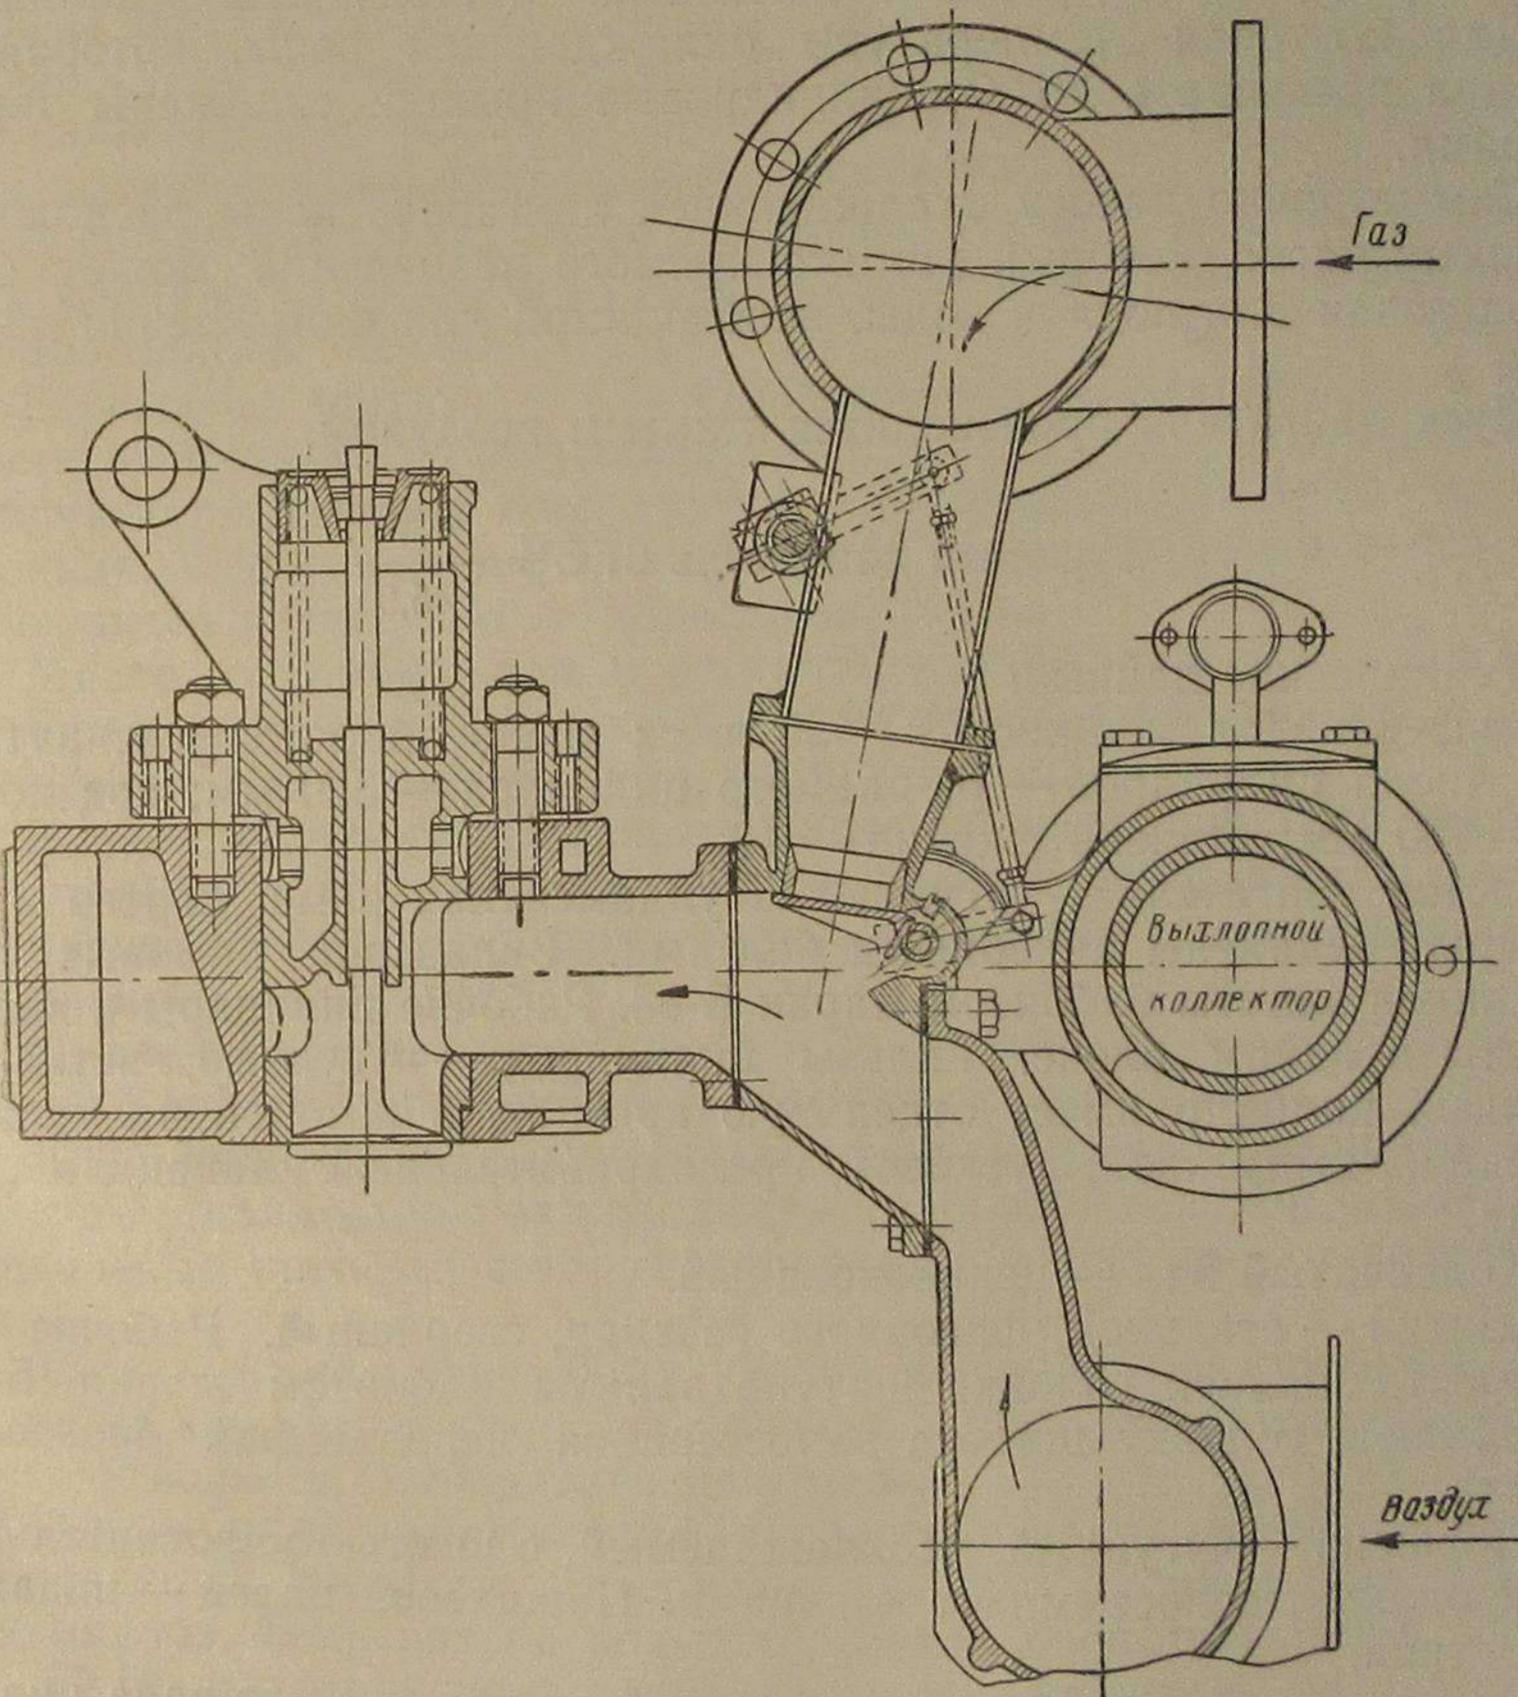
Смеситель двигателя 6ГСЧ $\frac{28,5}{24,0}$
